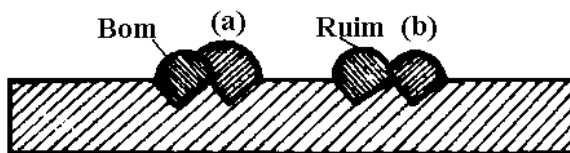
Cordões depositados numa soldagem de enchimento.
